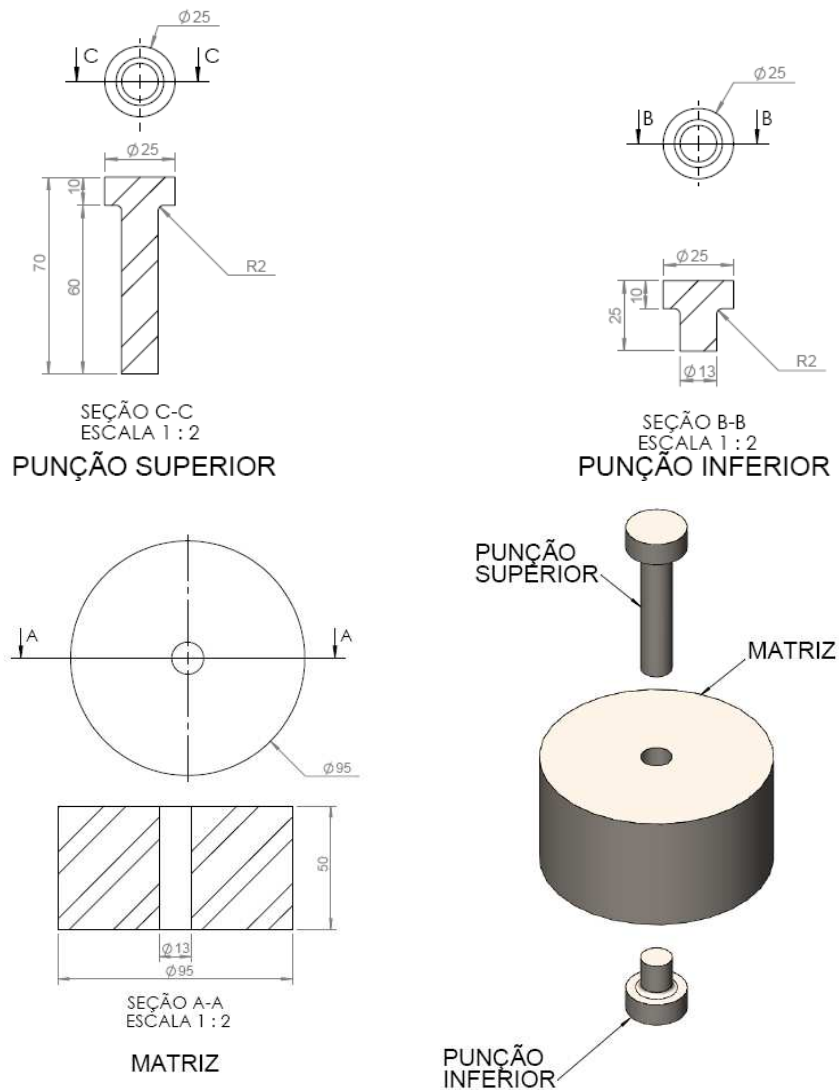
Desenho Técnico do Ferramental de compactação cilíndrica
